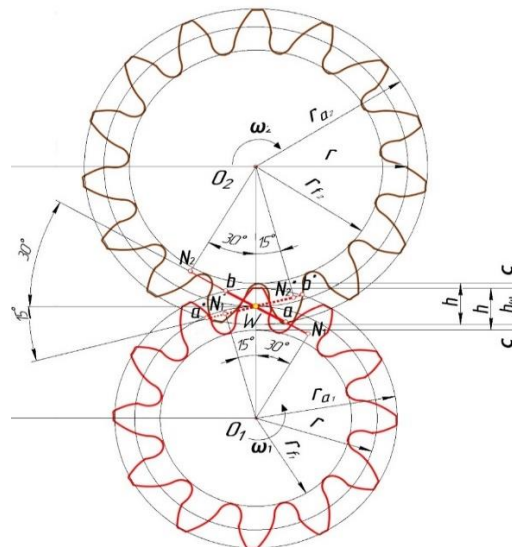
Геометрические параметры зубчатой передачи с несимметричными зубьями
